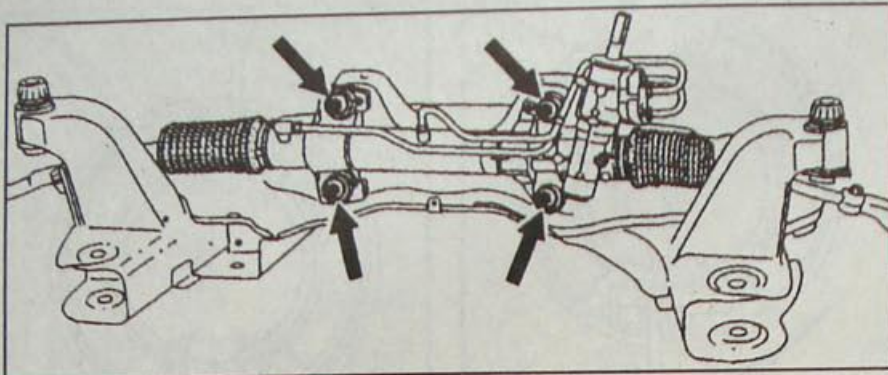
Расположение гаек крепления картера рулевой передачи
